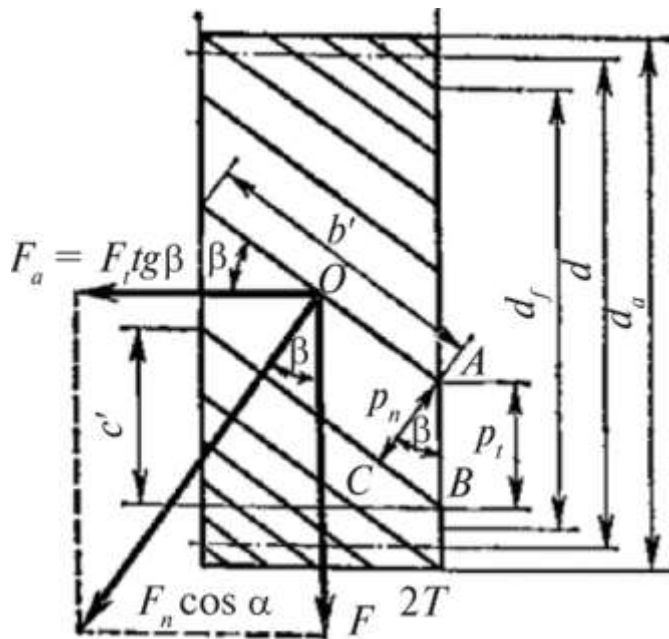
Геометрические соотношения косозубой цилиндрической передачи
